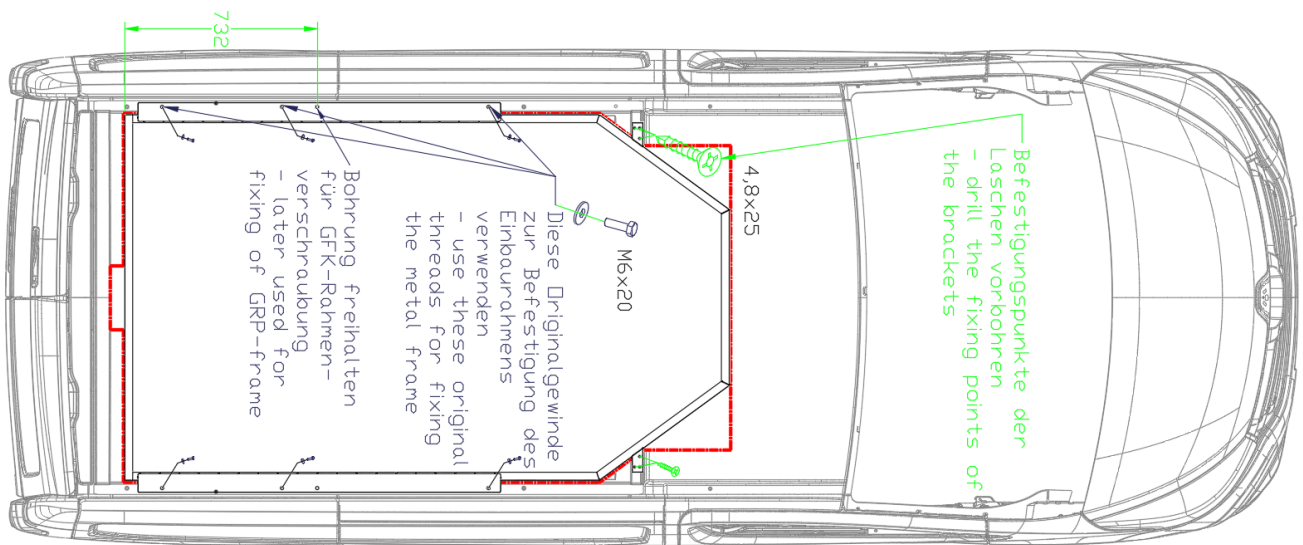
Einbaurahmen - Verschraubungspunkte Fahrzeug-Originalgewinde und Laschen / metal frame – fixing points of original vehicle threads and brackets [A0003929]
